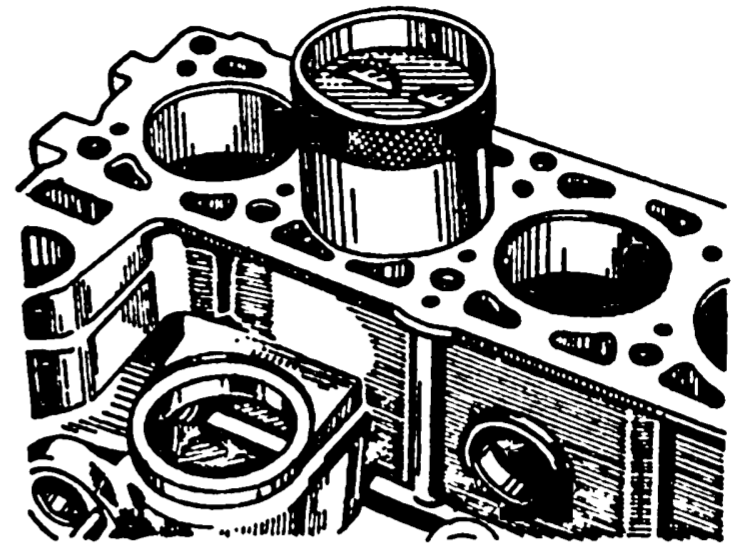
Установка поршня с поршневыми кольцами в цилиндр при помощи монтажной втулки из набора 02.7854.9500
